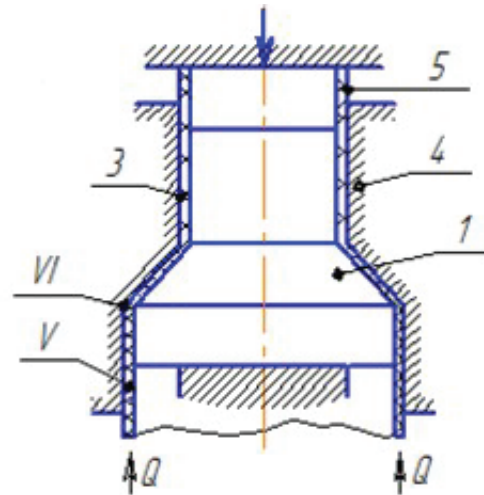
Роздавання трубчастої заготовки з всебічним підпором
